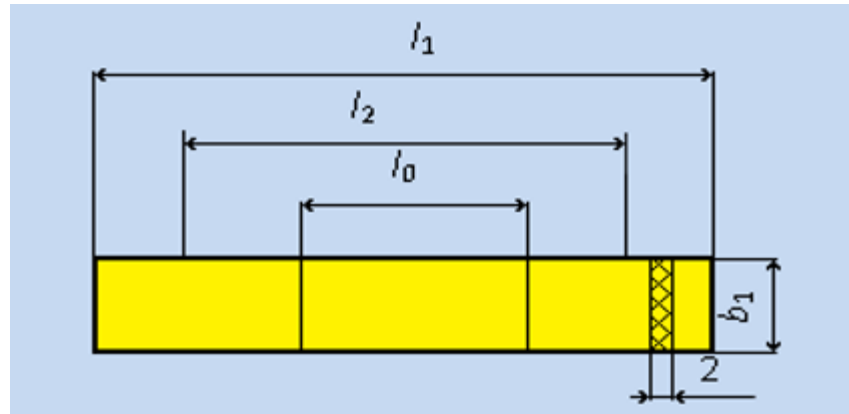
Размеры образца полиэтиленовой пленки со швом для разрыва (числовые значения размеров пленки приведены в таблице 3.4)
